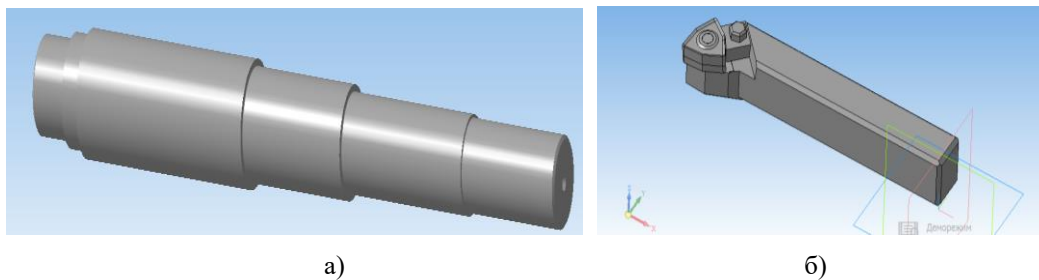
Рисунок 2.4 – а) заготовка; б) інструмент
